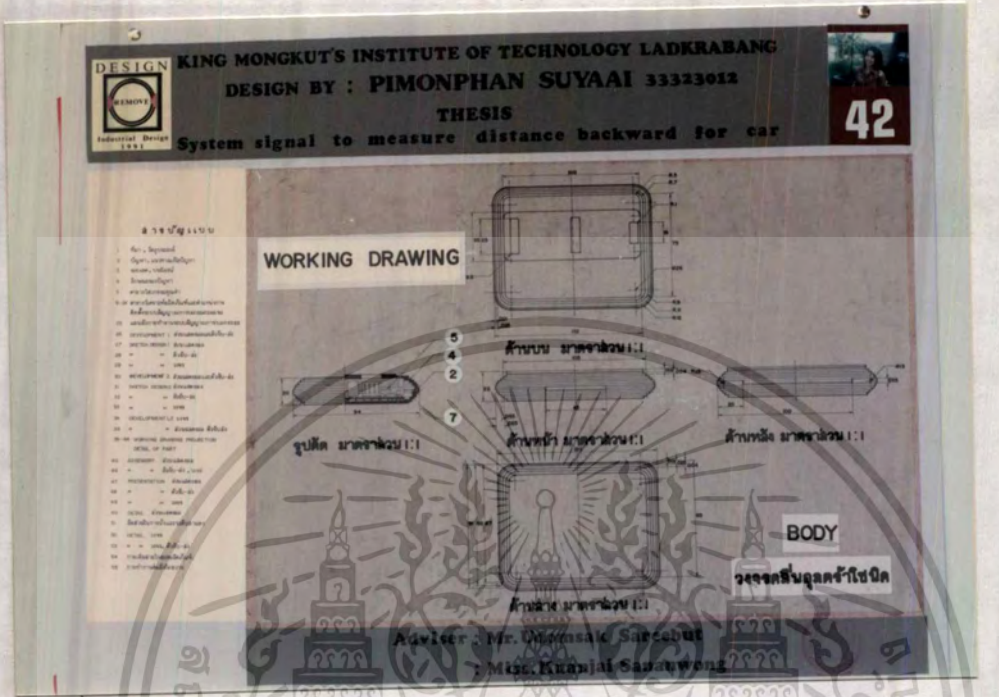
WORKING DRAWING / DETAIL OF PART
